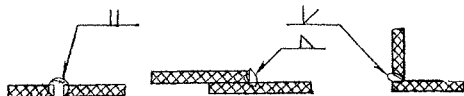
Виды сварных соединений, применяемых при сварке воздуховодов из винипласта
